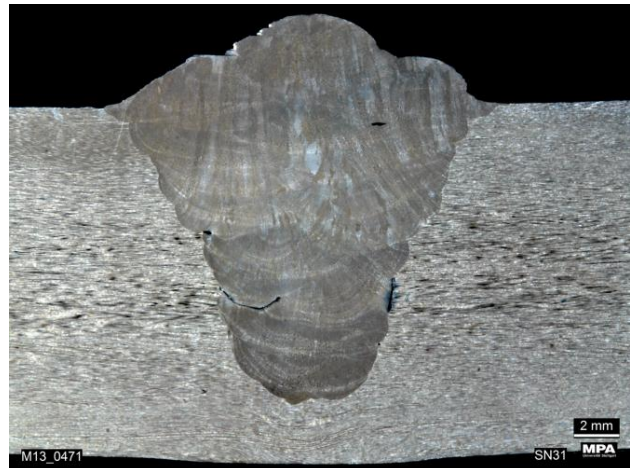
Schweißnaht unter Einfluss eines Permanentmagnetes ($H = 80 \text{ mT}$ in der Naht) geschweißt, Schweißfehler durch erschwerte Schweißbedingungen aufgrund des starken Magnetfelds.
